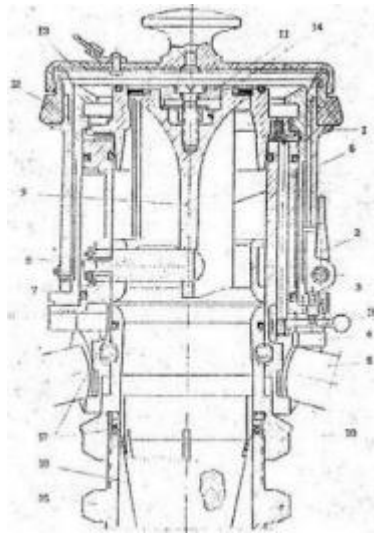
Накінечник закритою заправки в зборі: 1 - зовнішній кожух; 2 - затиск; 3 - зовнішній корпус; 4 - фланець; 5 - рукоятка; 6 - внутрішній корпус; 7 - ролики; 8 - вісь роликів; 9 - клапан; 10 - муфта; 11 - шайба клапана; 12 - гумове кільце; 13 - кришка; 14 - стопорні кільця; 15 - перехідник; 16 - важіль стопора; 17 - ущільнення; 18 - сітчастий фільтр
